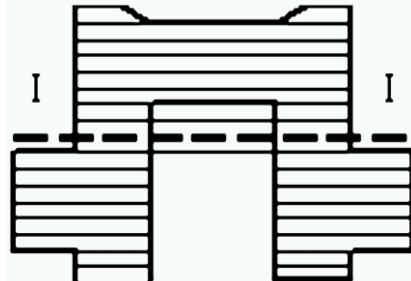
Схема макроструктури колінчастого вала, виготовленого вирізуванням з плоскої заготовки
